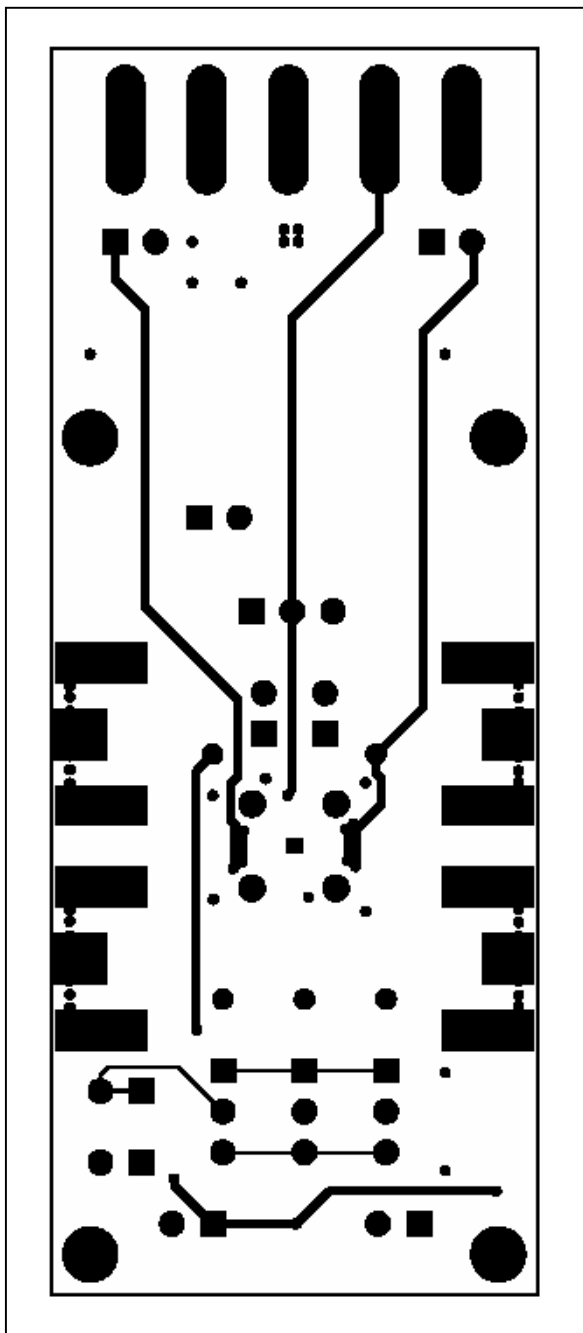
MAX3805 PC 板布局 – 焊接层
